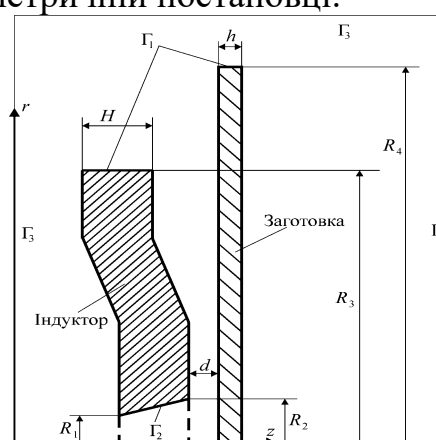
Розрахункова схема для чисельного розв'язання (меридіональний переріз індуктора та заготовки)
